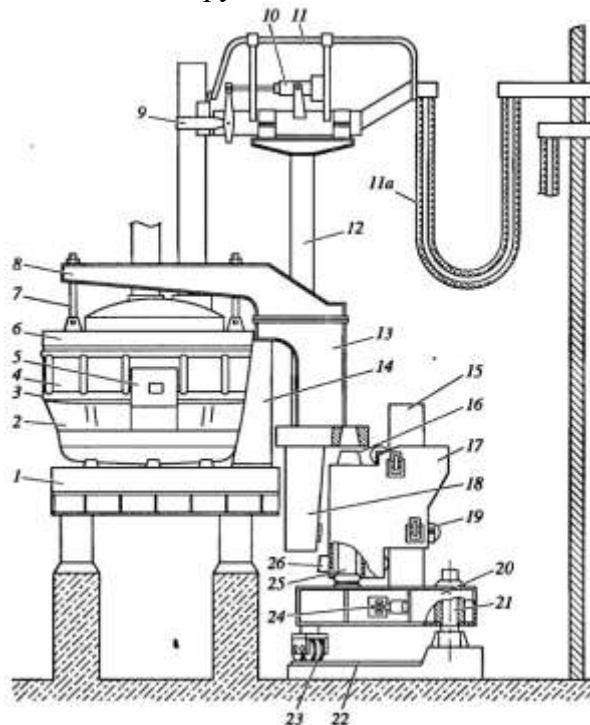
Печь с опорой механизмов подъема — поворота свода на отдельный фундамент
